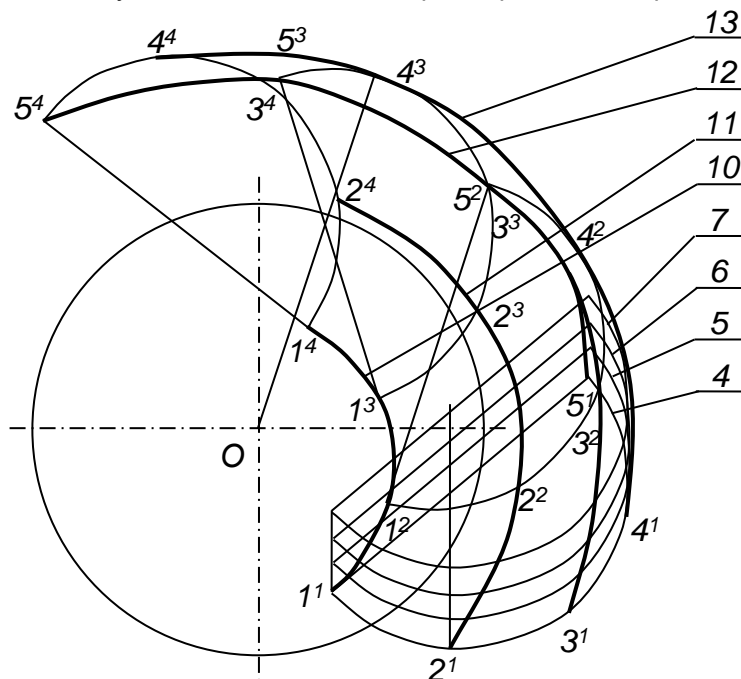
Схема лемішно-полищевого картоплекопача, вид робочої поверхні
